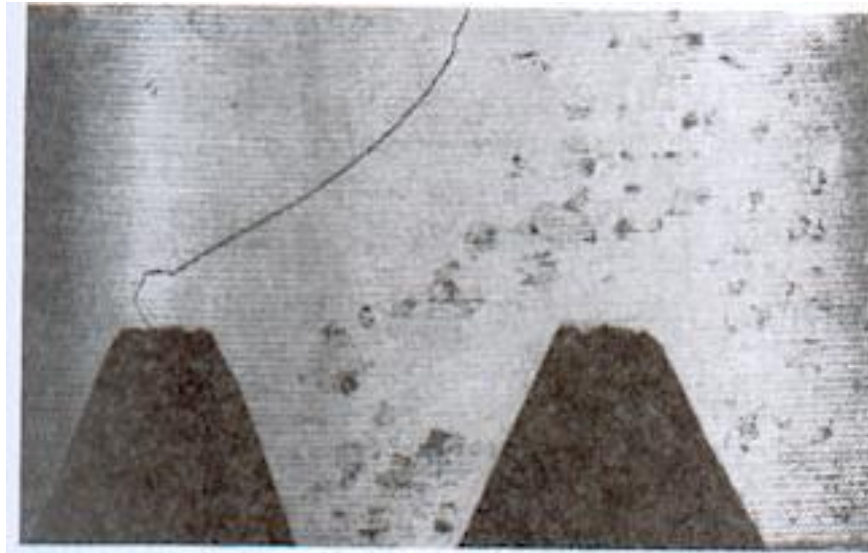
Fissuration au pied de la dent [87]
